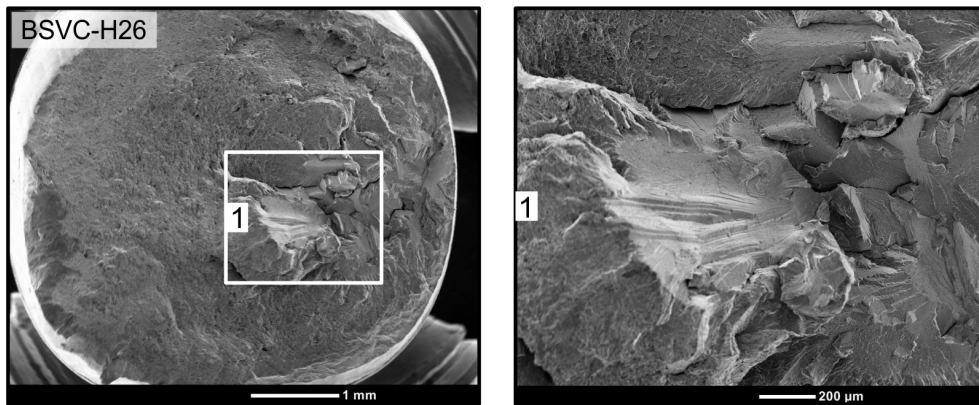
Probe BSVC-H26, REM-Aufnahmen, 550 °C, Bruch im Schweißgut
